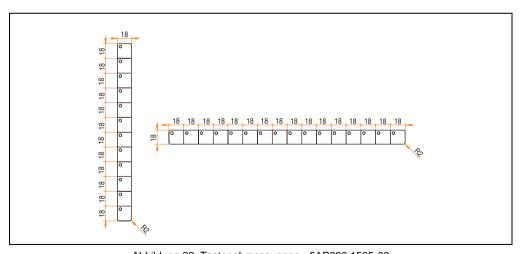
Tastenabmessungen - 5AP880.1505-00
